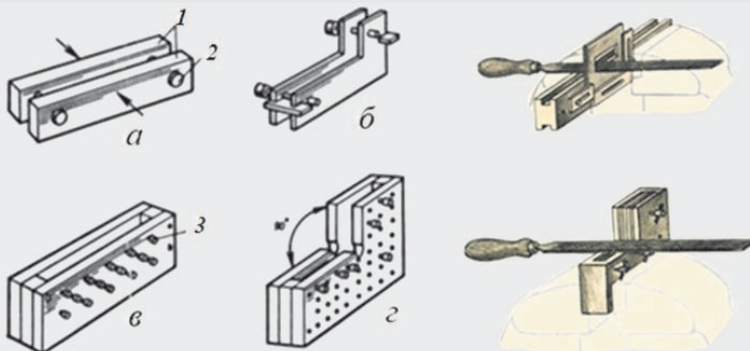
Обпилювальні рамки і намітки: а — рамка для плоского обпилювання; б — рамка для обпилювання прямих кутів; в — позначка для плоского обпилювання; г — позначка для обпилювання внутрішніх кутів. 1 — планка, 2 — штифти, 3 — гвинти
